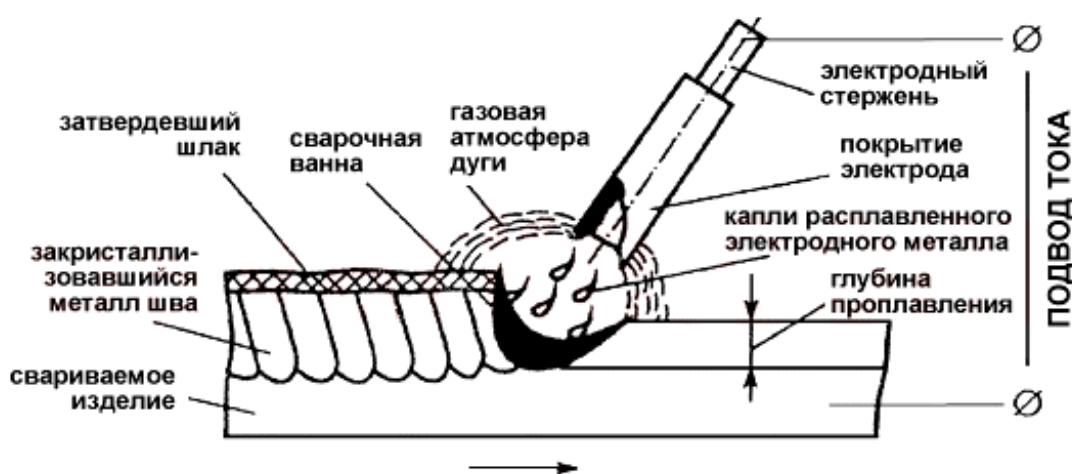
Схема процесса ручной дуговой сварки штучными электродами
